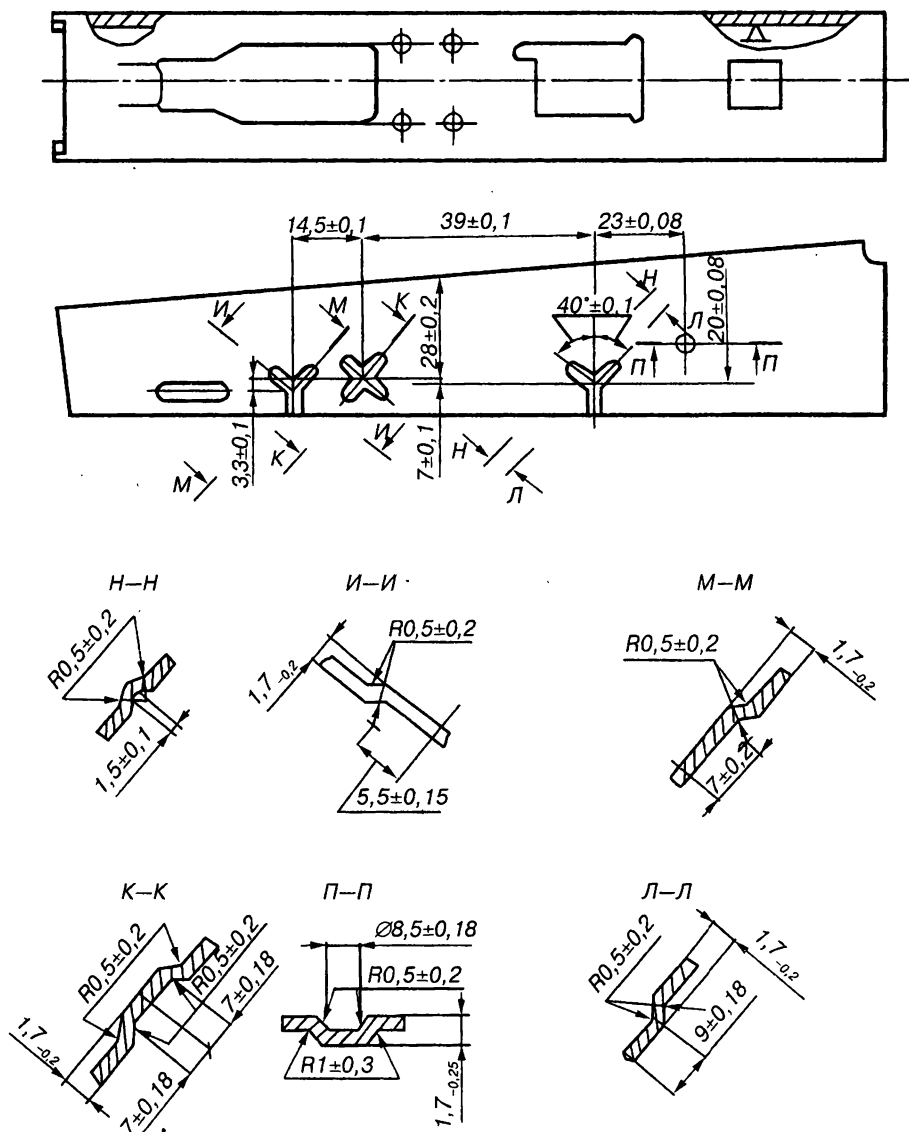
Рельефная формовка крестовины и выдавок на прессе К2324 с усилием 260 кН
